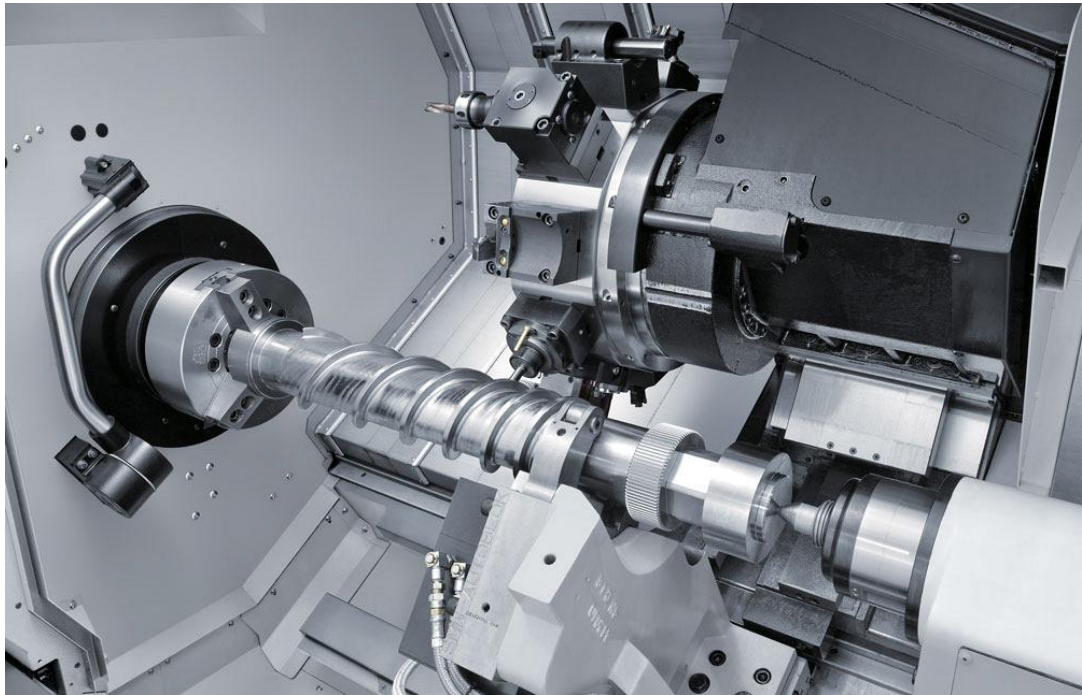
Використання люнета як додаткові опори при токарному обробленні деталі [12]
